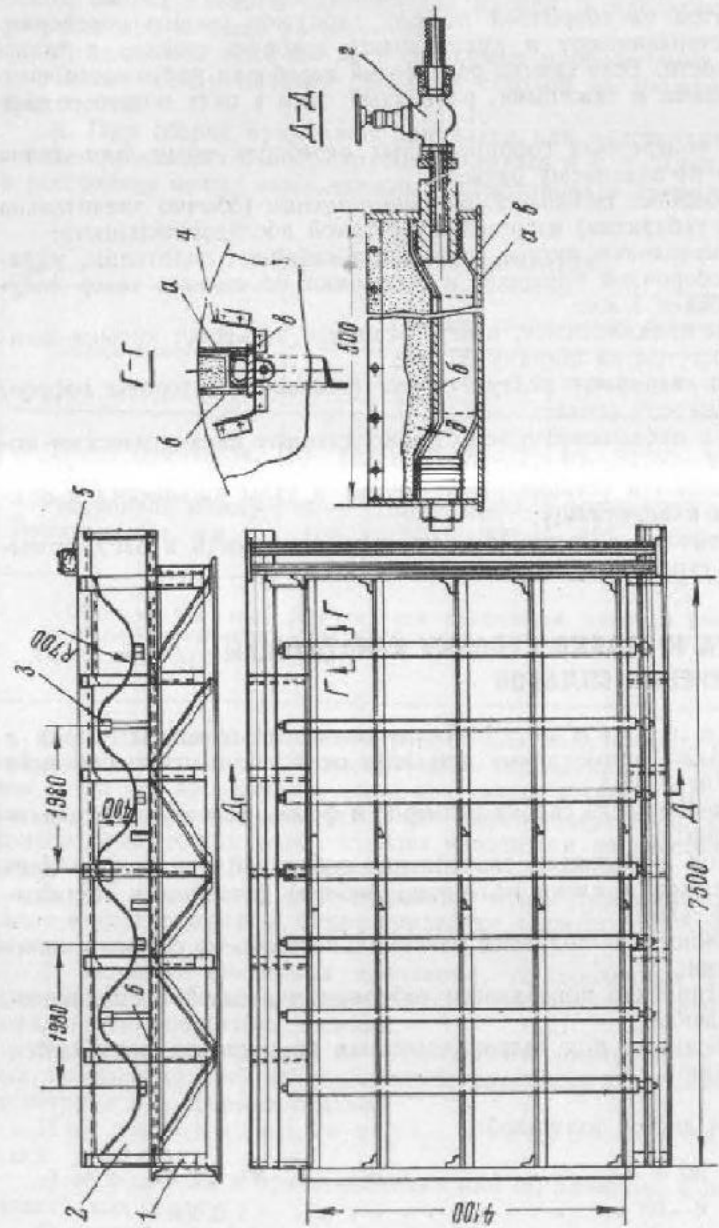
Постель для сборки и сварки узлов полотнищ гофрированных переборок.
